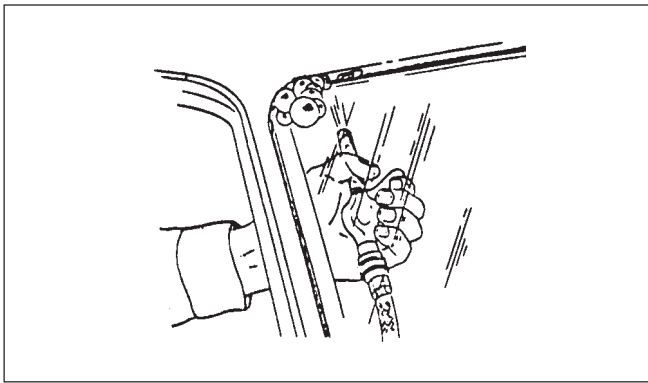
Testul cu aer și soluție spumantă asupra parbrizului
